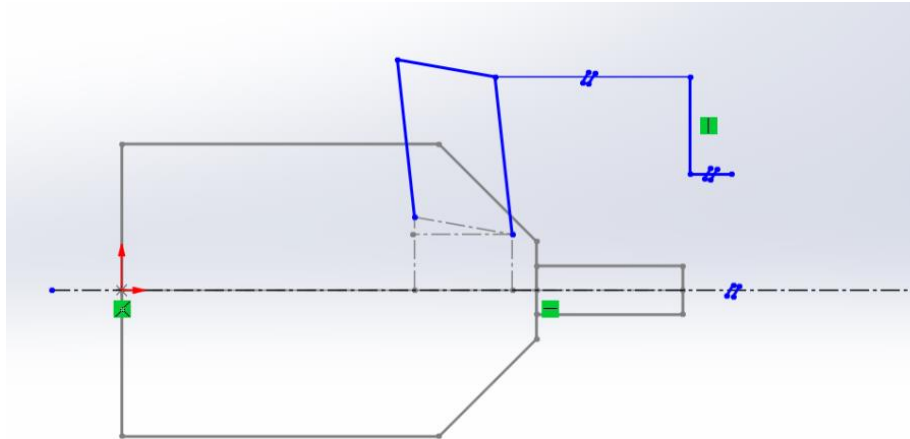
3.Paralelismo entre elementos de la pinza y eje de la herramienta
